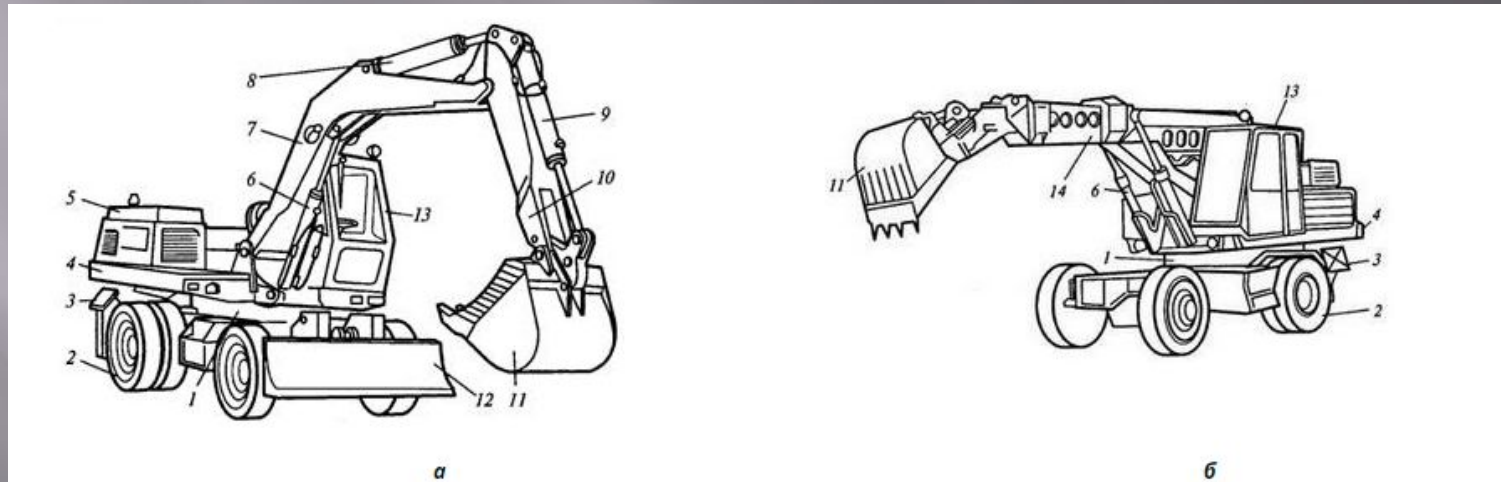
Одноковшовые гидравлические полноповоротные экскаваторы с жесткой подвеской рабочего оборудования: 1 — опорно-поворотное устройство; 2 — пневмоколесное ходовое устройство; 3 — выносная опора; 4 — поворотная платформа; 5 — силовая установка; 6,8,9 — гидроцилиндры стрелы; 7 — стрела; 10 — рукоять; 11 — ковш обратной лопаты; 12 — бульдозерный отвал; 13 — кабина машиниста; 14 — телескопическая стрела
